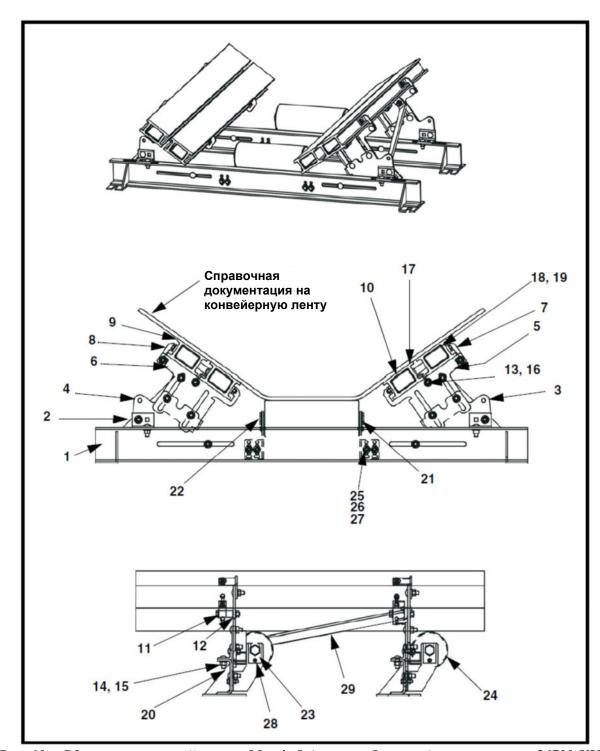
Сборка скользящей опоры Martin® (с двумя балками), номер детали 36700-XXX
